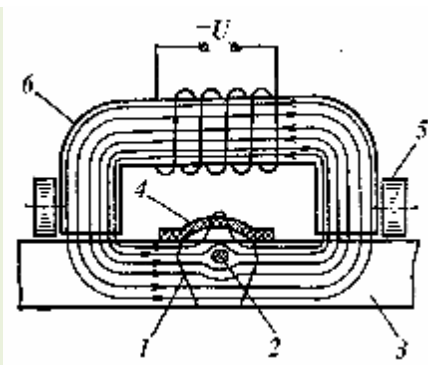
Схема намагничивания сварного шва вместе с магнитной лентой:
